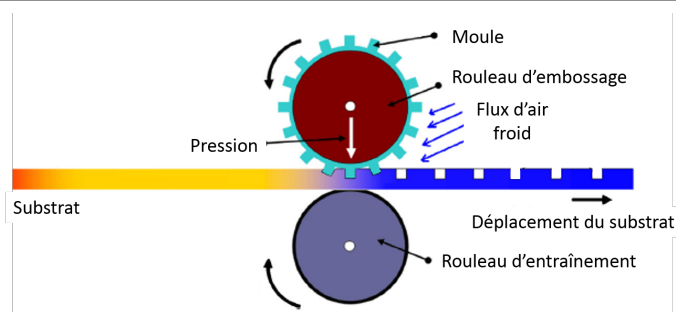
Procédé d'embossage en Roll-to-Roll (adaptée de [8])
